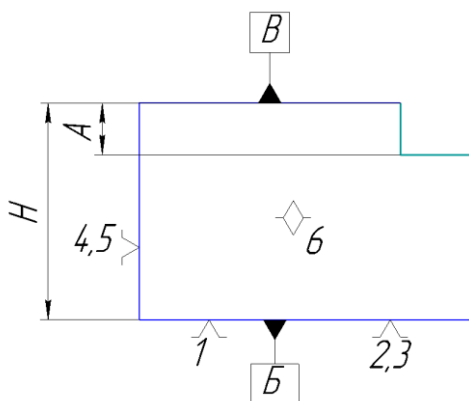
Схема фрезерования уступа при установке заготовки по плоскости и двум боковым сторонам
